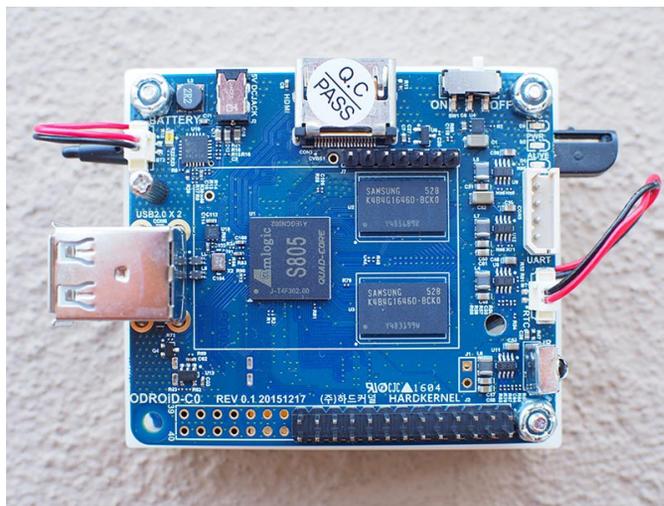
Toda la soldadura está completada. Ten en cuenta que el cabezal de doble fila simplemente se ha soldado a 26 pines GPIO.
